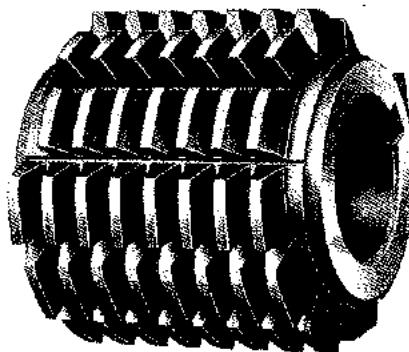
Fresa-madre para tallar dientes de engranajes (Pratt & Whitney Co.)
